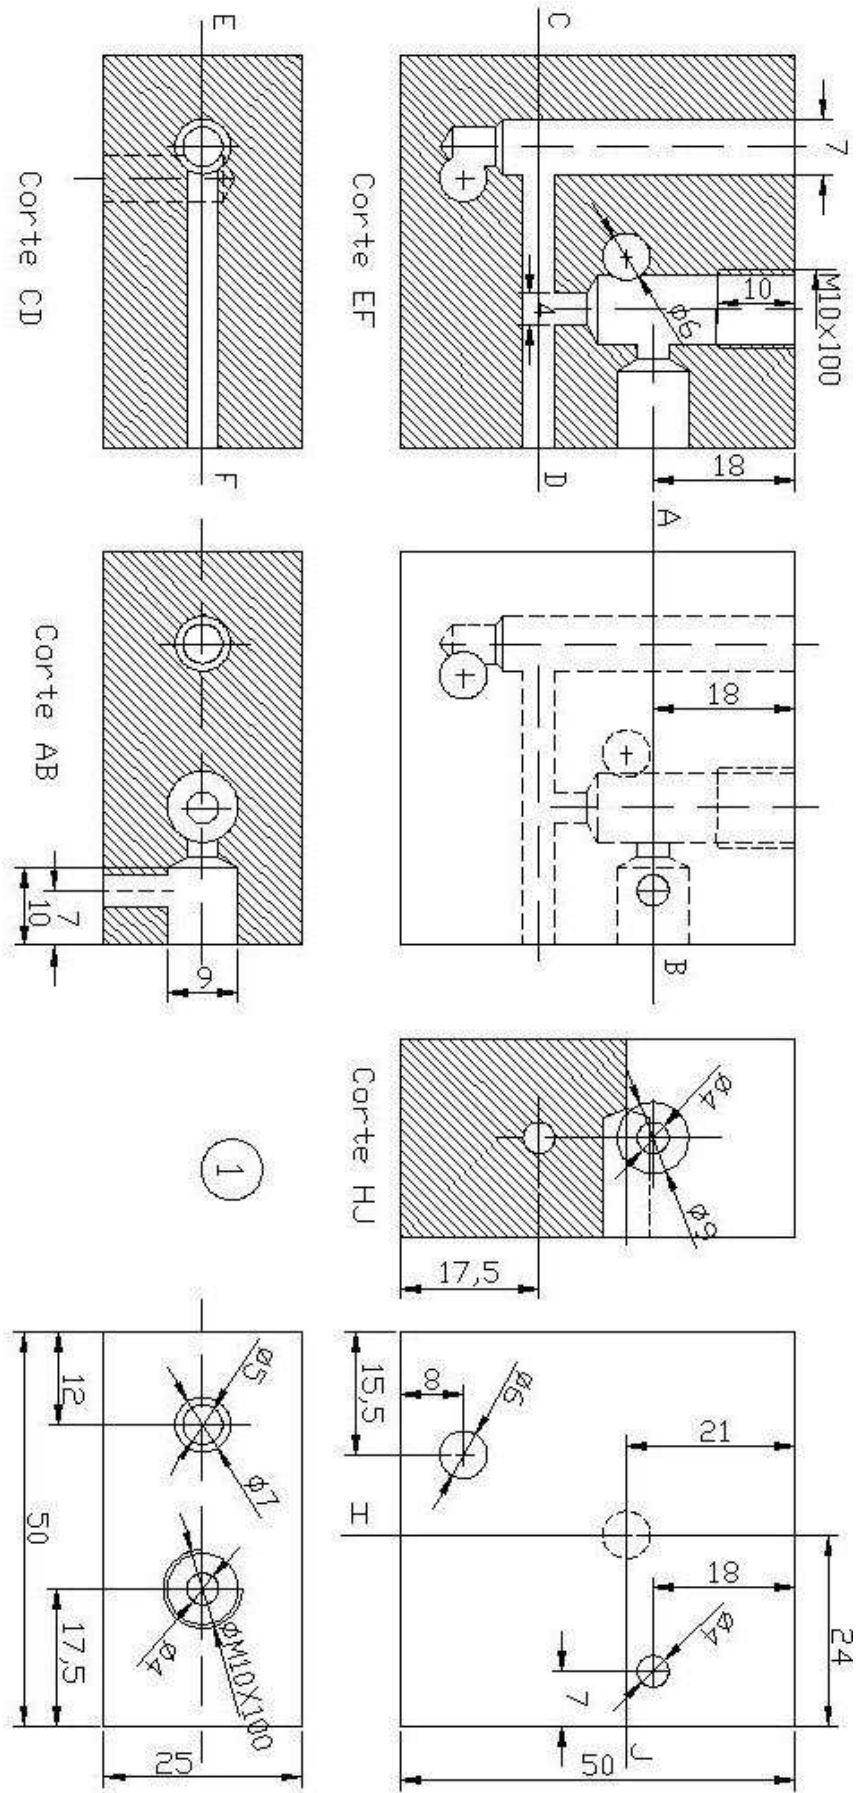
hidráulico para dobrar tubos, vista da peça 1
